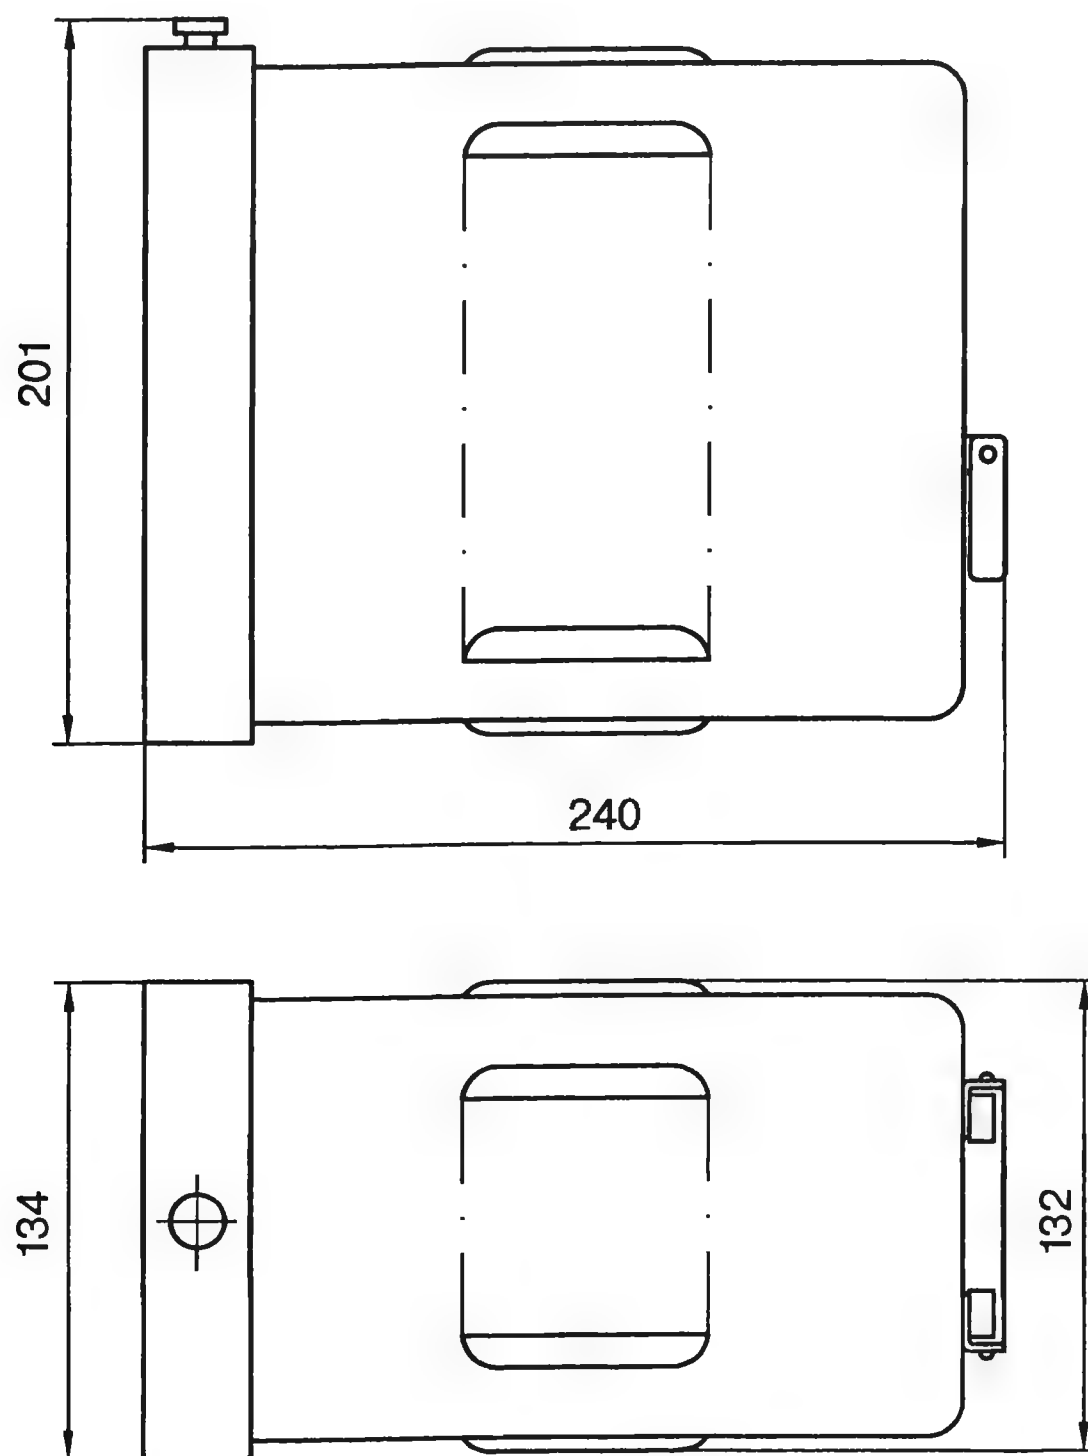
Габаритный чертеж приемников ПП, ППМ
